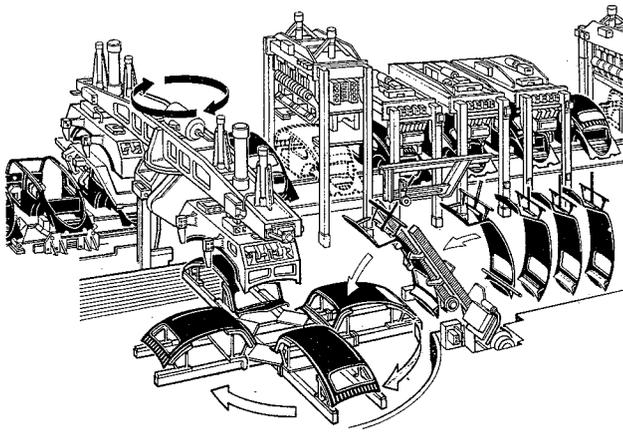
Einlegestation des Daches in einer Karosserie-Montagestraße.
